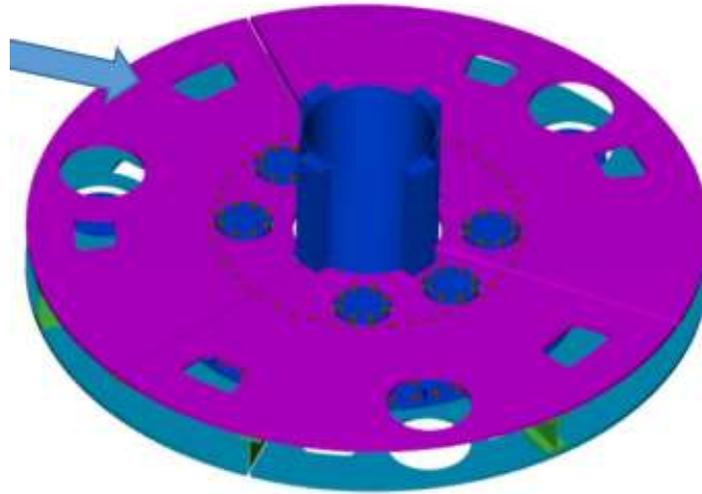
Instalación placa superior. Tomado de «Instructivo para Montaje de Drive de Espesador de Cuajone» (16 p. 20)
